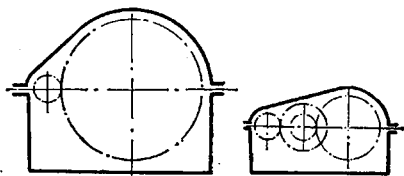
Схема одно- и двухступенчатого редукторов с одинаковым передаточным числом.
